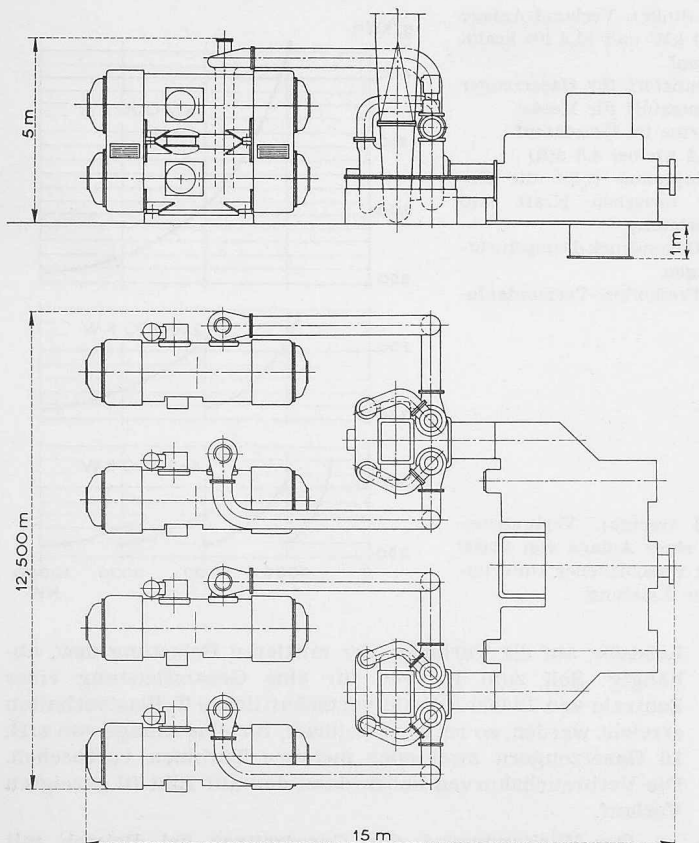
Schiffsanlage für 22 000 PS mit vier Zwillingsgaserzeugern von 540 mm Motordurchmesser
